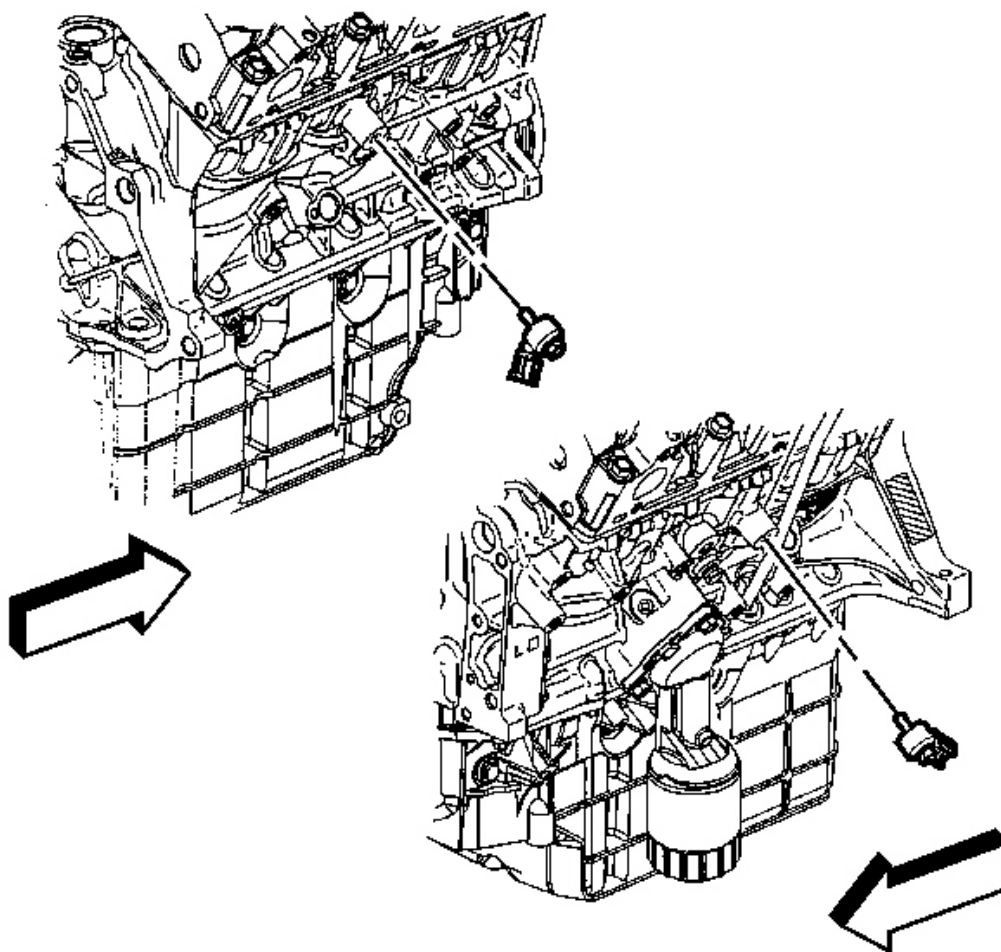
Localización de aceite del motor Indicador de presión Interruptor de
